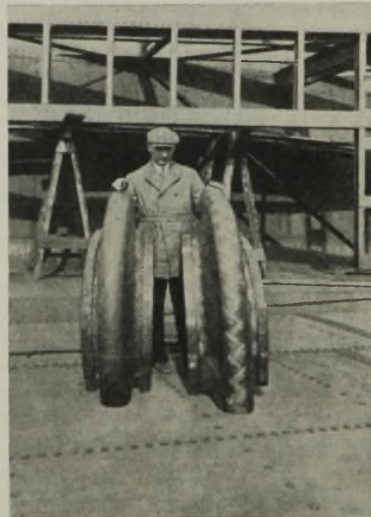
Krümmen der Kupferwelle, Außenseite; links gepreßter, rechts geschweißter Krümmer.
